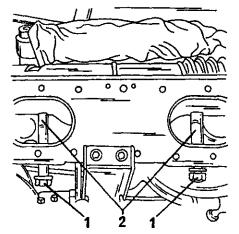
Расположение двух болтов крепления (1) зубчато-реечного рулевого механизма. Между ними вставлены распорки (2).
